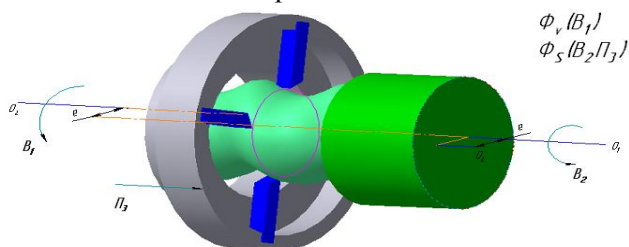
Кинематические схемы обработки круговых винтовых поверхностей с помощью резцовой головки
